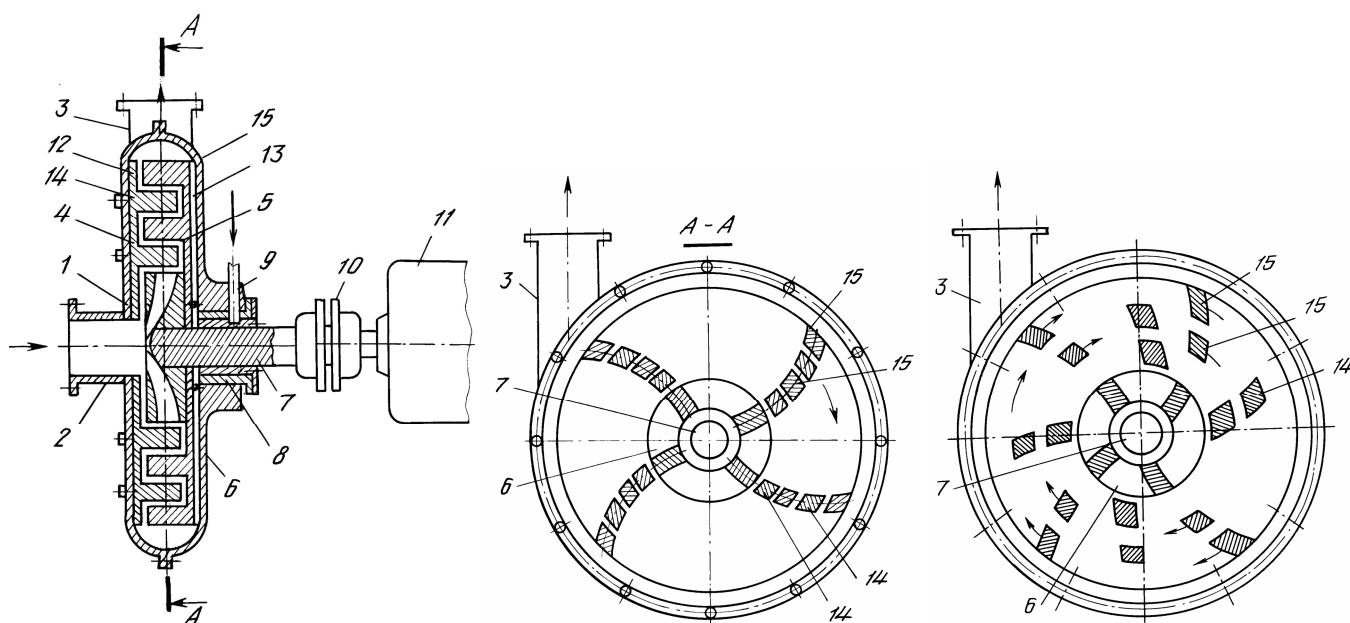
Конструкція роторного гідравлічного млина
